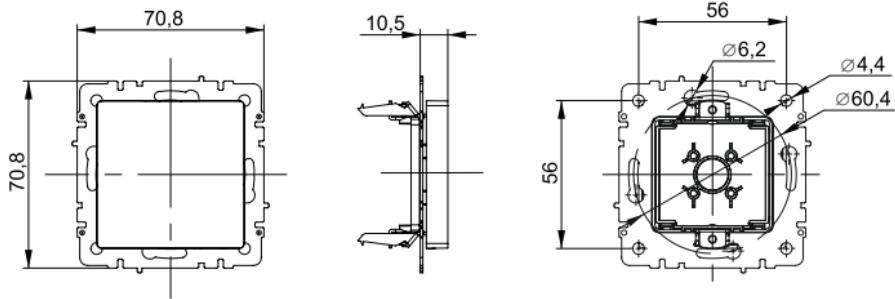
Габаритные и установочные размеры заглушки / Figure 2 – Overall and installation dimensions of the plug /
